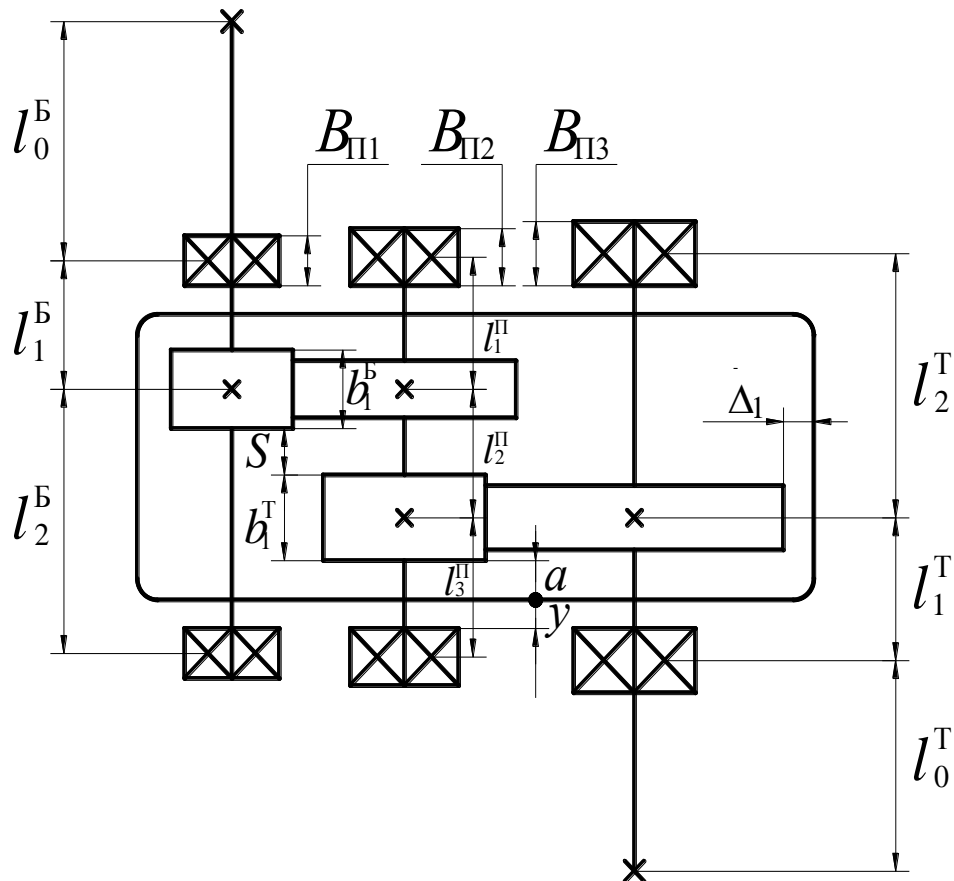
Схема двухступенчатого цилиндрического редуктора
